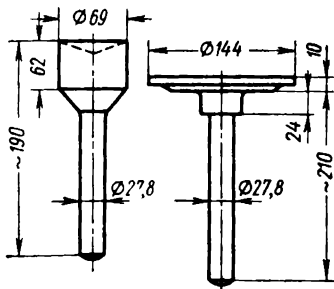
Двухпереходная штамповка поковки ведущего вала
